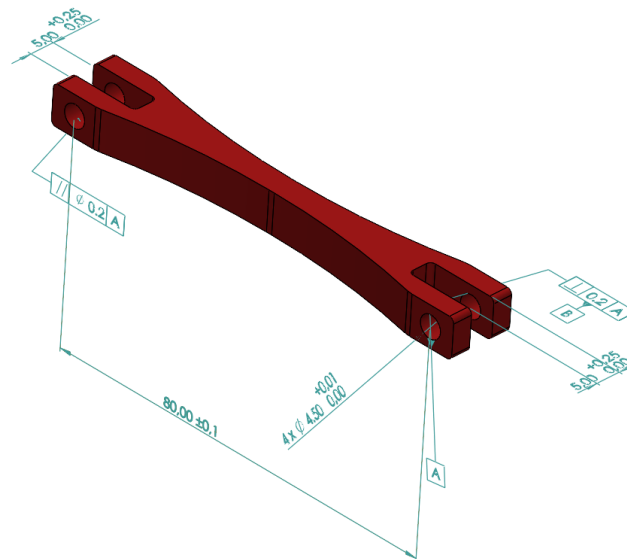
Tolerancias dimensionales “Barra 2” dedos
